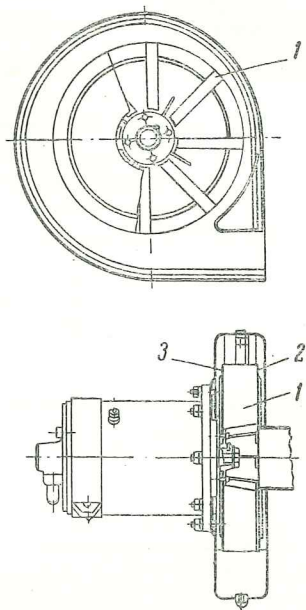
Схема электровентильатора установки ЗИС для автомобиля ЗИС-21
